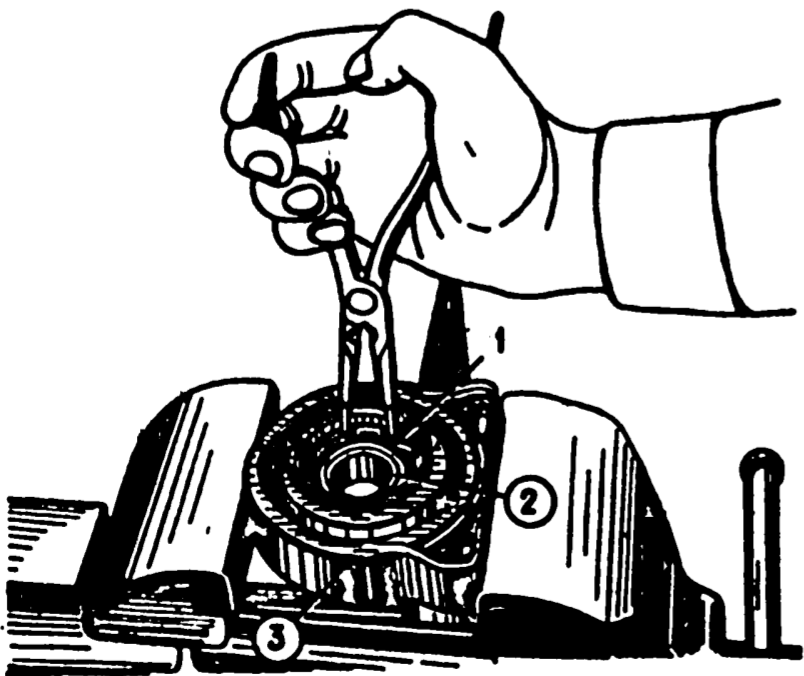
Извлечение стопорного кольца подшипника упругой опоры: 1 - стопорное кольцо; 2 - подшипник; 3 - упругая опора
